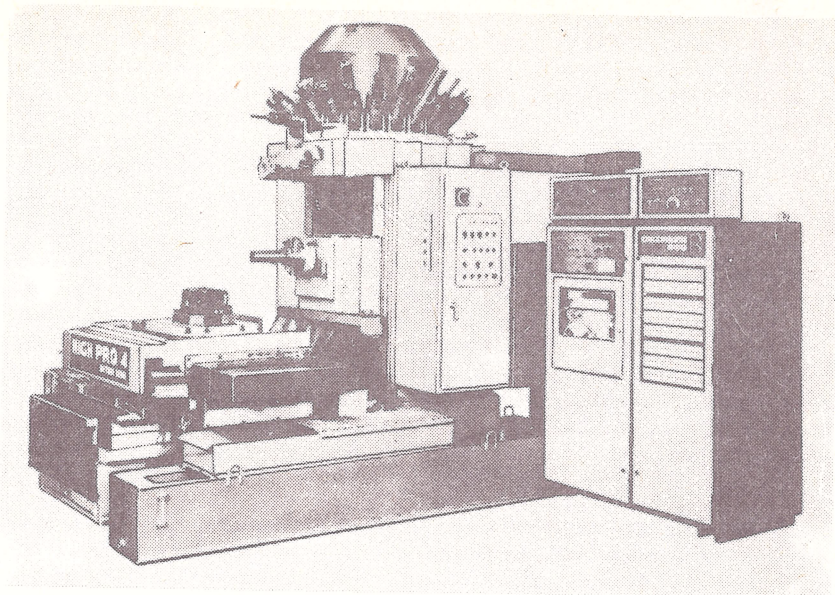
Металлообрабатывающий центр «Хич Про-4» (High Pro-4, Япония)
